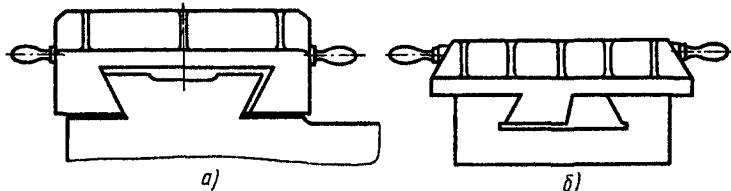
Способы проверки направляющих типа «ласточкин хвост»: а — шабровочная плита для проверки основания, б — шабровочная плита для проверки наклонной поверхности
